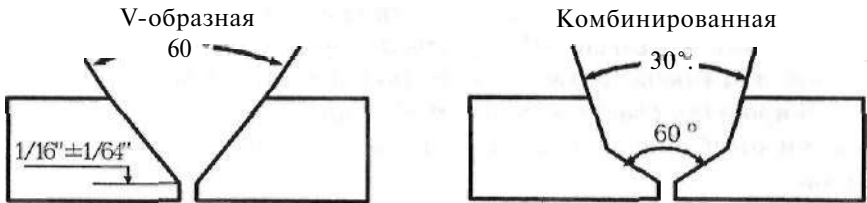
Разделка кромок для сварки процессом STT
